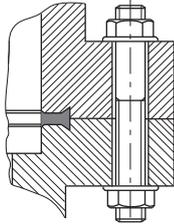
Flanschverbindung CF-F, Stiftschraube und Durchgangsbohrung
